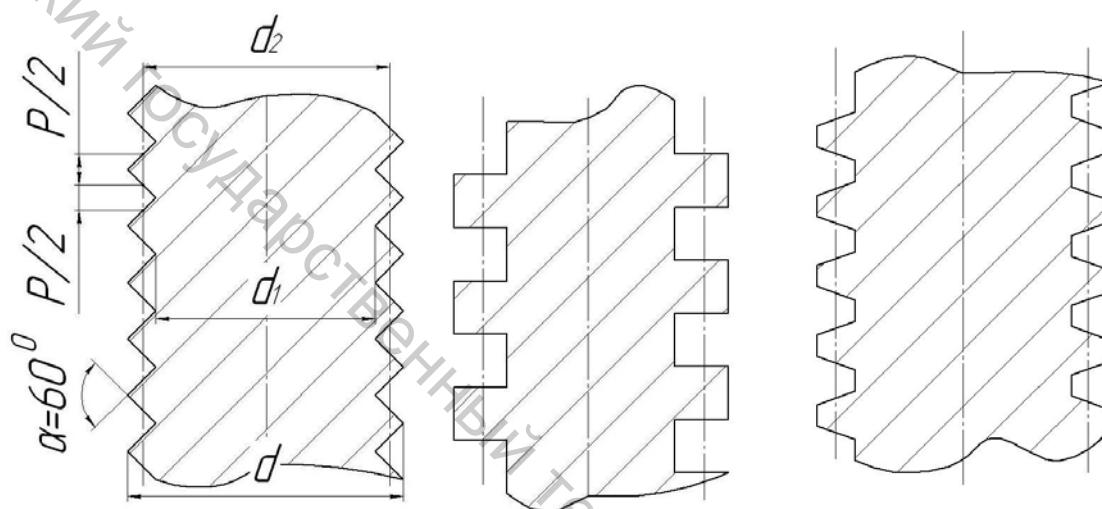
Аксиальные сечения резьб и их основные размеры
